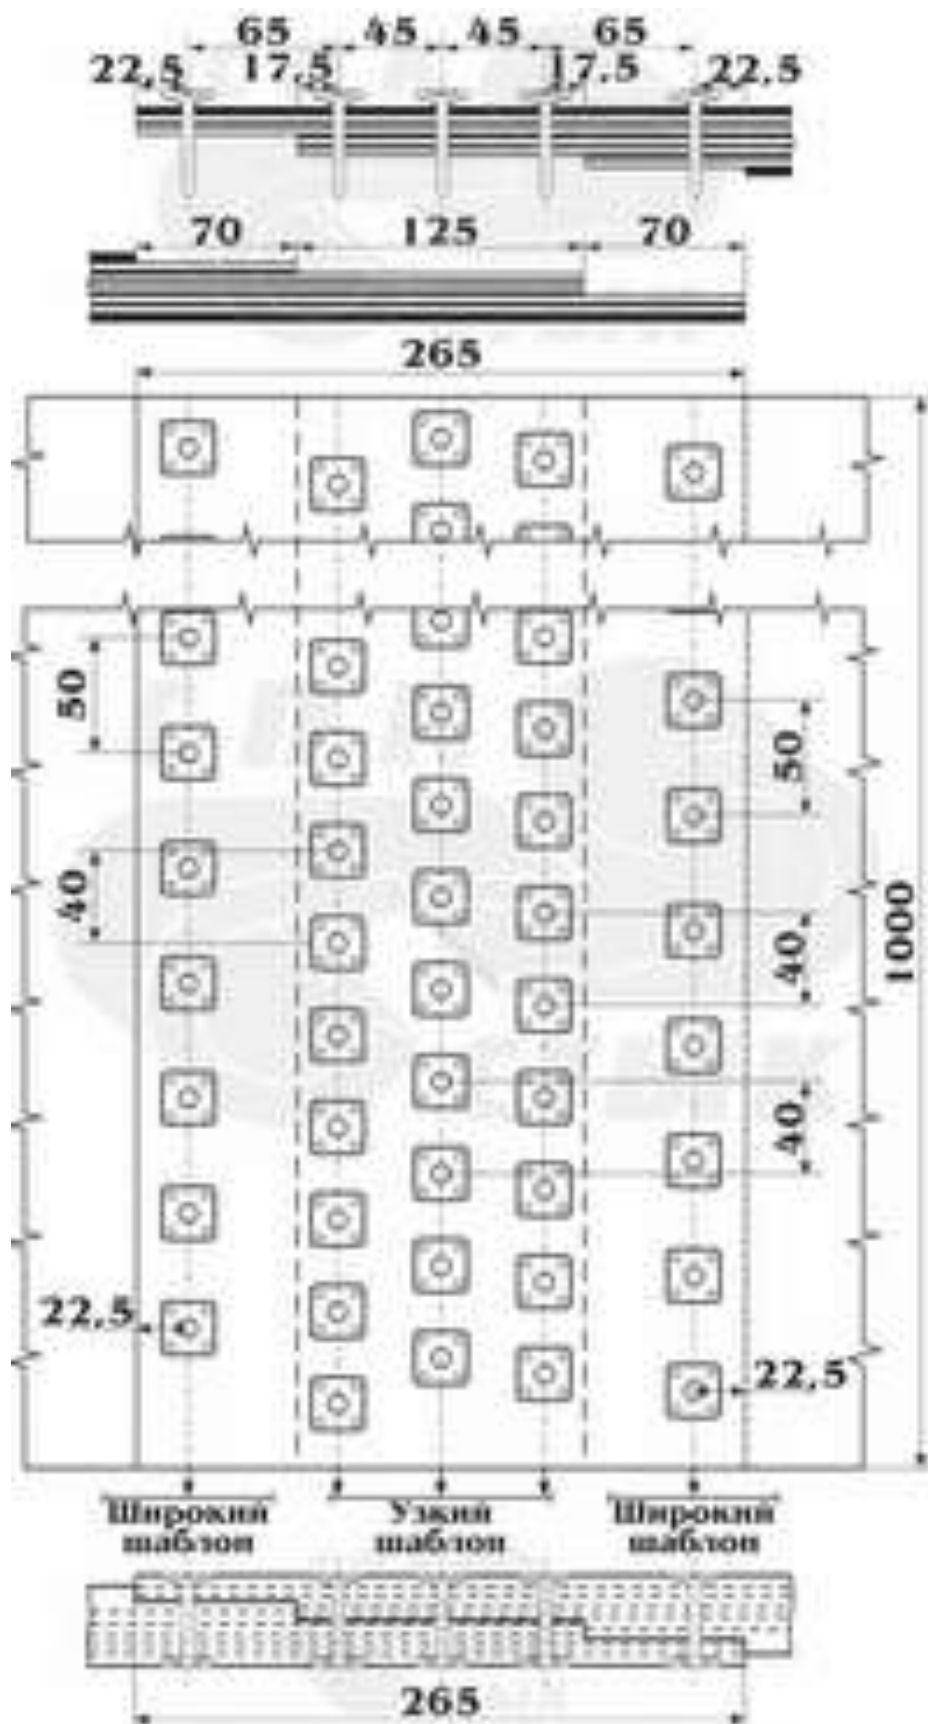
Схема 5-рядного стыка и разделки конвейерной ленты прочностью до 1260 кН/м
